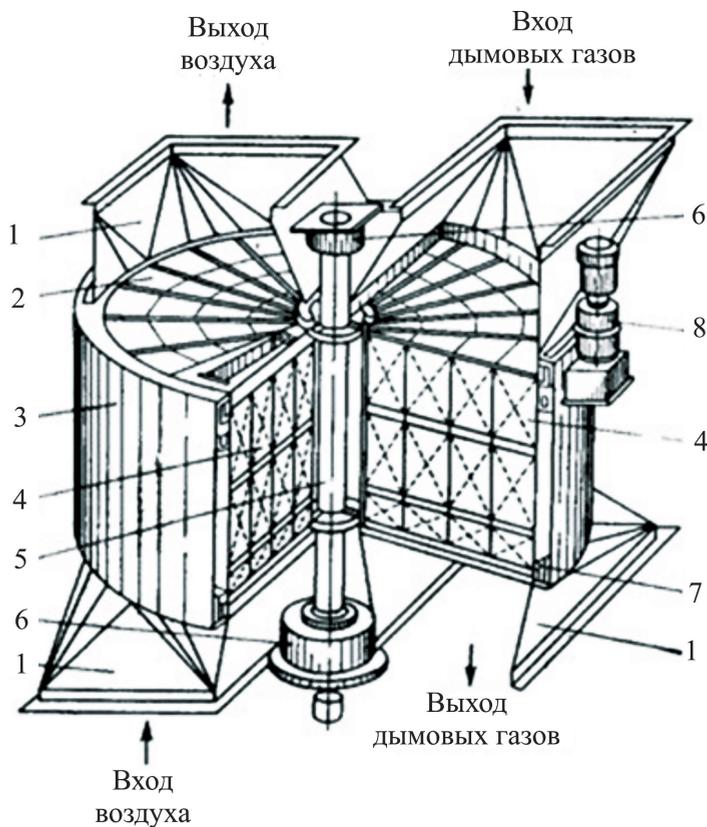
Вращающийся регенеративный воздухоподогреватель типа РВВ-41М:
